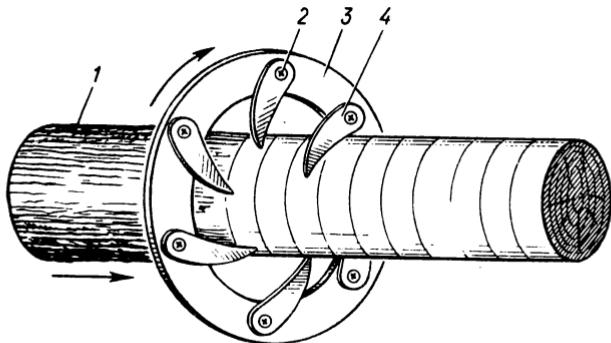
Принципиальная схема работы окорочного станка роторного типа:
